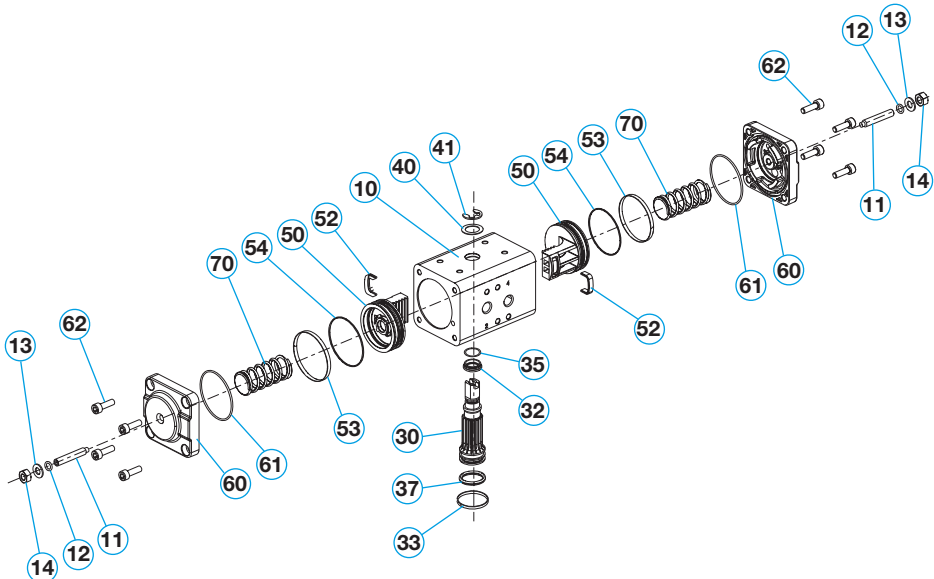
Explosionszeichnung aller Einzelkomponenten Schwenkantrieb actubar
